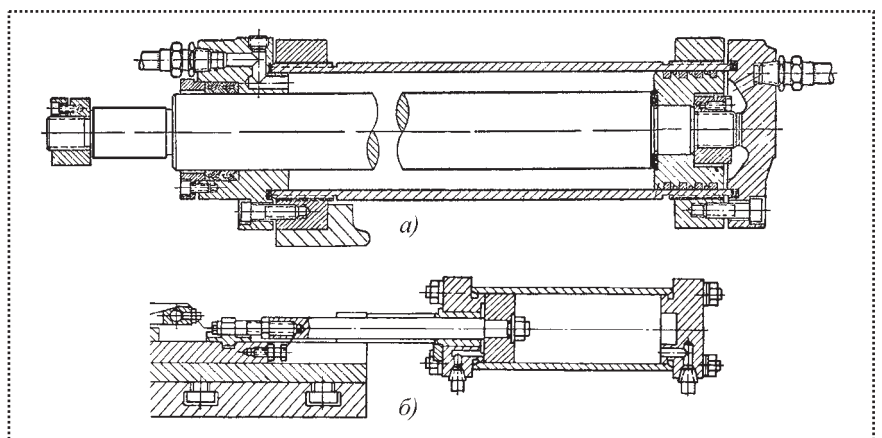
Примеры использования длинномерных цилиндрических деталей: а – рабочий цилиндр гидропривода возвратно-поступательного движения; б – привод механизма досылателя заготовок в зону сборки
